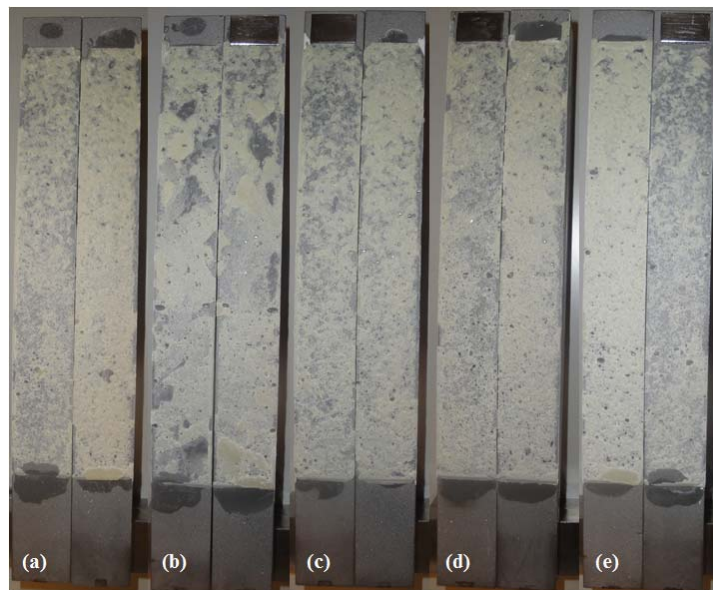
Rotura do adesivo Sikaforce[®] 7752 no ensaio DCB (a) Provette 1 (b) Provette 2 (c) Provette 3 (d) Provette 4 (e) Provette 5
